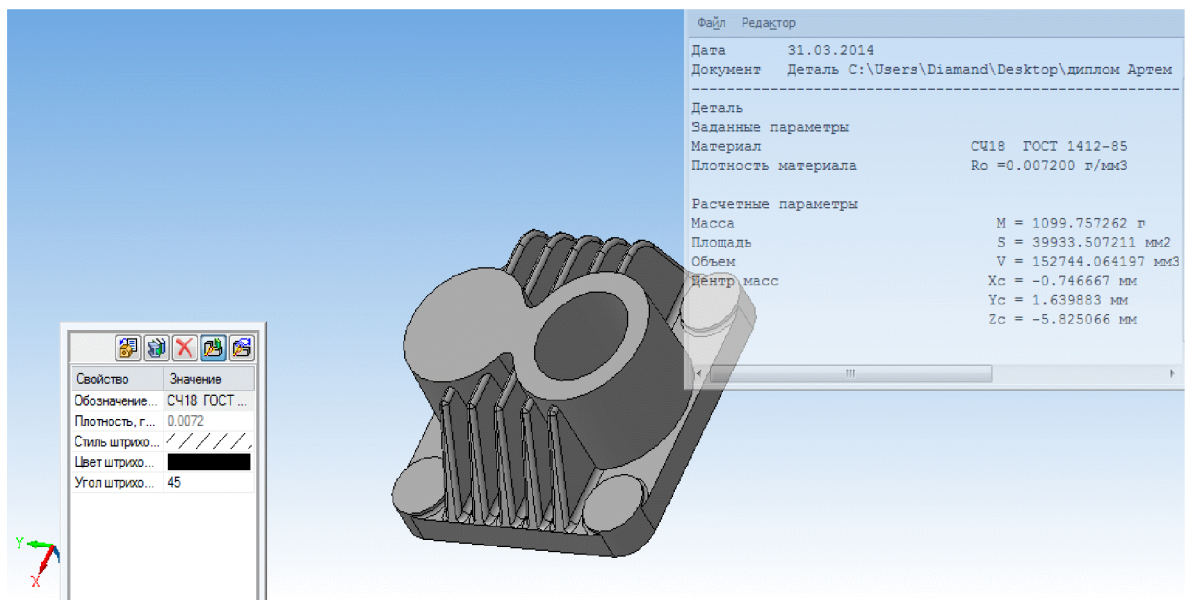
Визначення маси вилівка «Корпус 21.10» за допомогою КОМПАС-3D»
